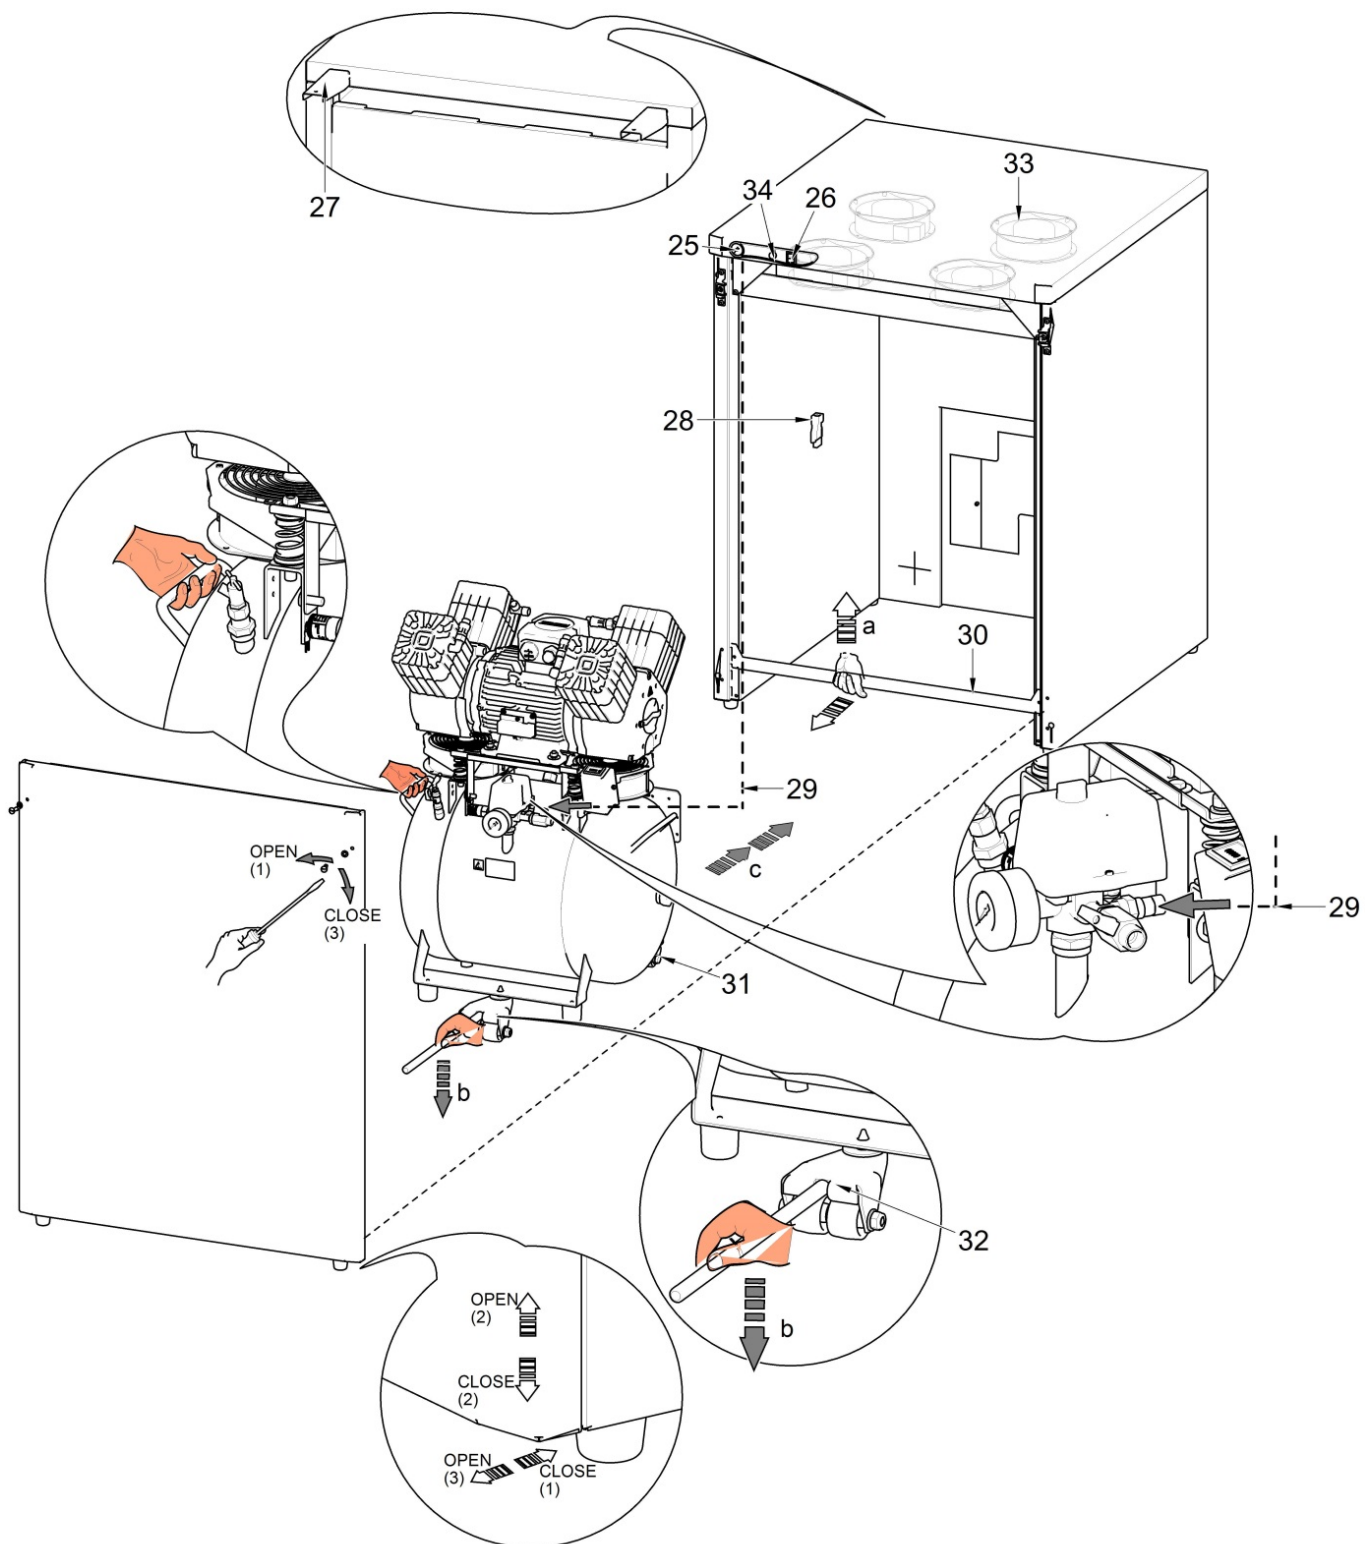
Kompresor s membránovou sušičkou (MD)
